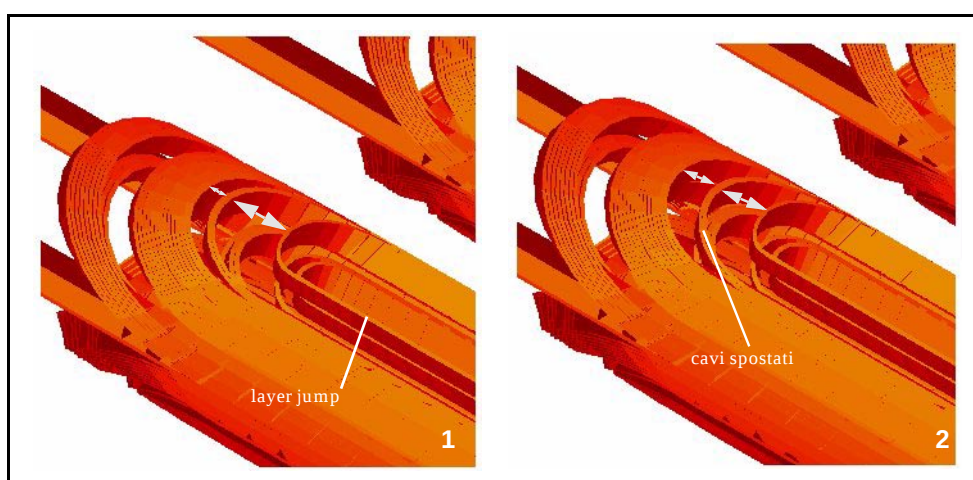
Aspetto della bobina lato connessione elaborato in ROXIE: (1)layout attuale dei conduttori; (2)layout modificato con lo spostamento di 10 mm dei conduttori 4&8 dello strato superiore.
